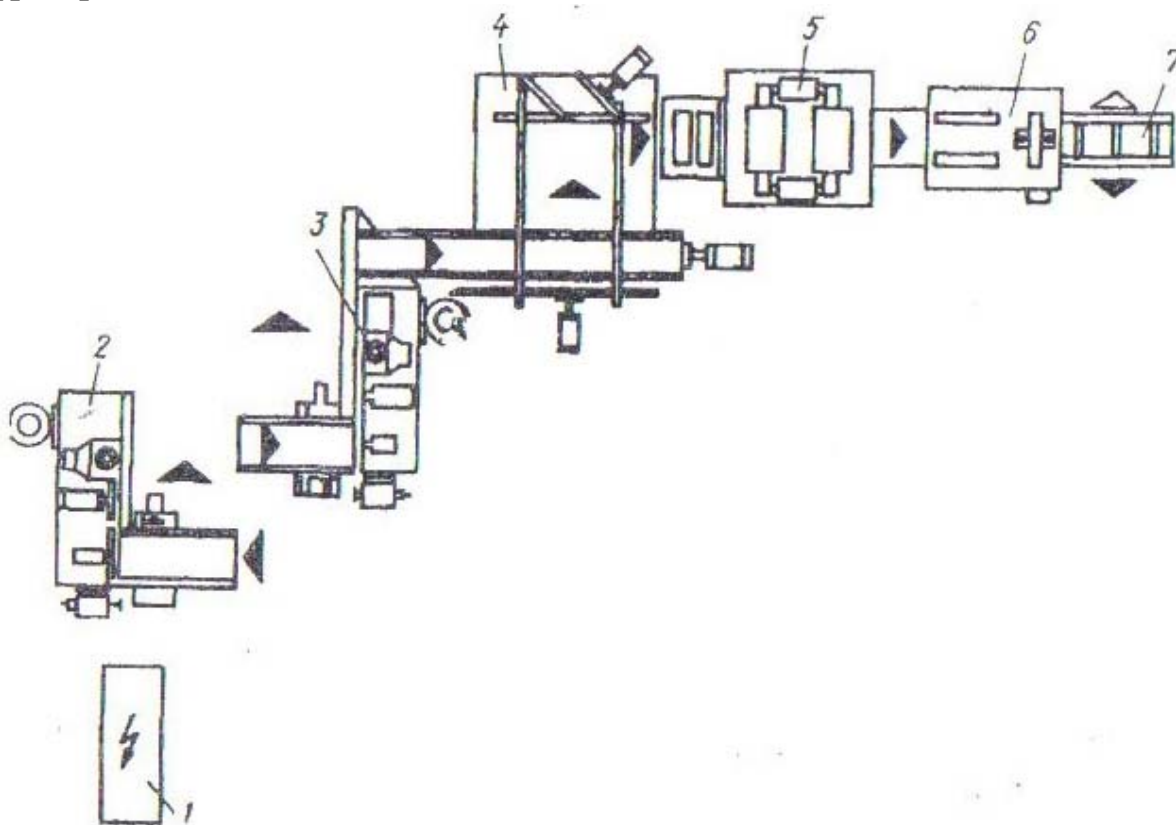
Схема линии склеивания заготовок по длине на зубчатый шип:
